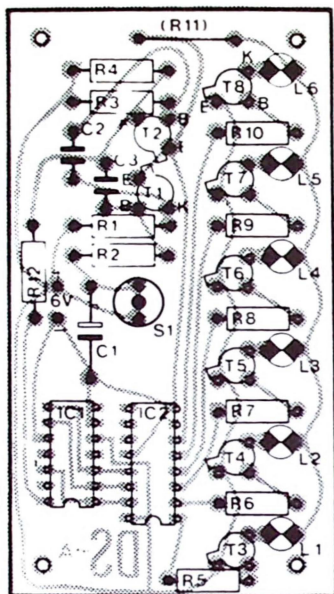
Bestückungsplan für den Elektro-Toto-Würfel mit Lampen.
